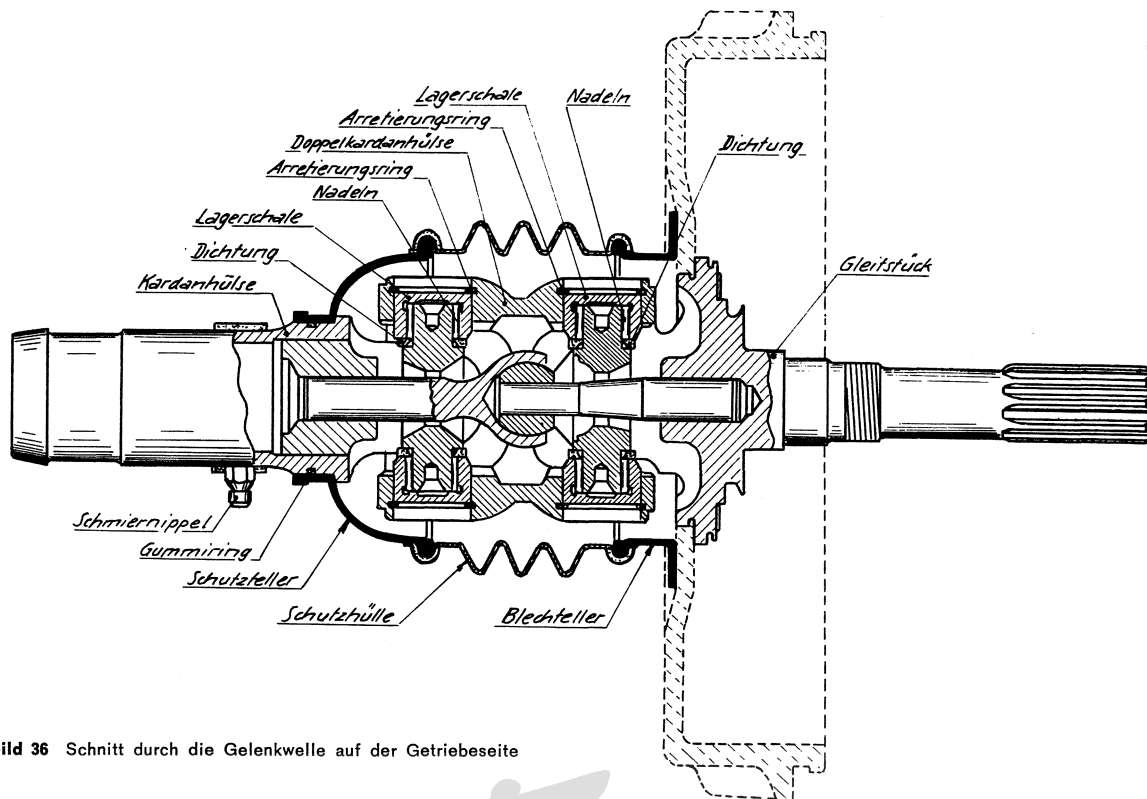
Schnitt durch die Gelenkwelle auf der Getriebeseite
